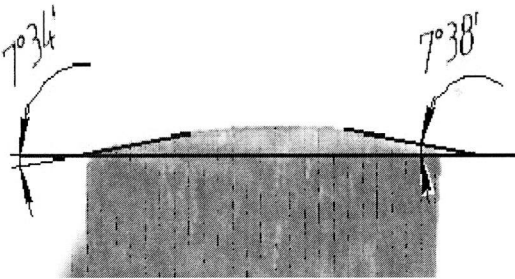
Зовнішній вигляд робочого торця породоруйнівної вставки після заточування
